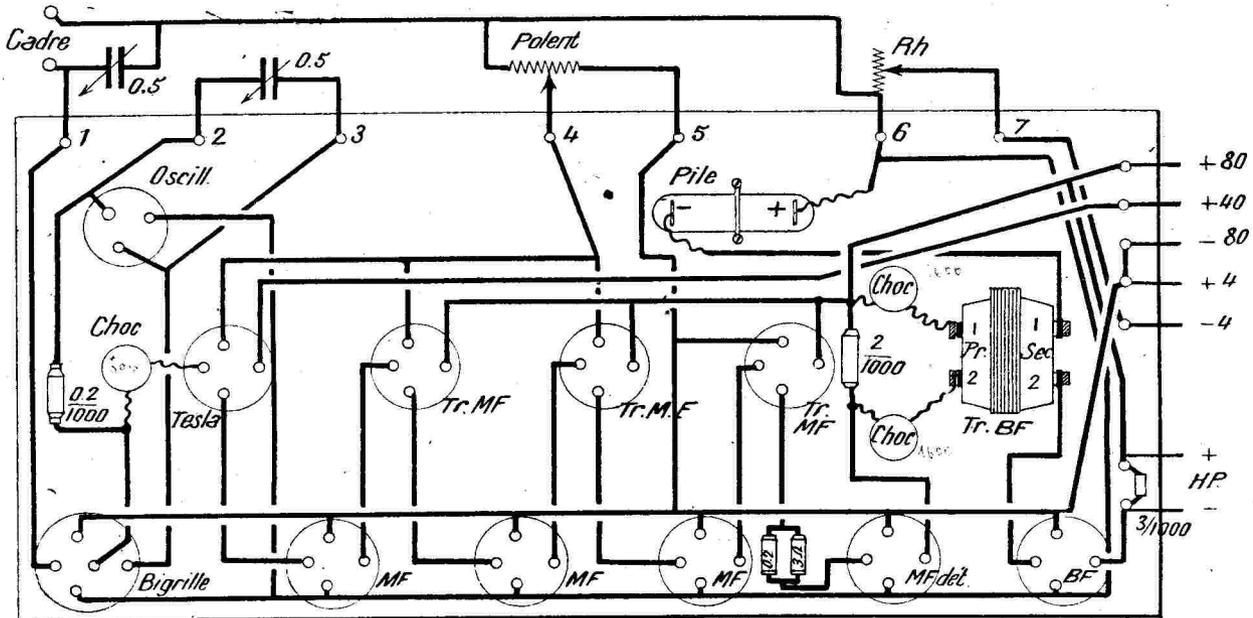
Disposition des lampes, supports des transformateurs M. F. et oscillatrice, transformateurs basse fréquence et condensateurs fixes, connexions et soudure sur la plaque à lampe : vue en-dessous.
